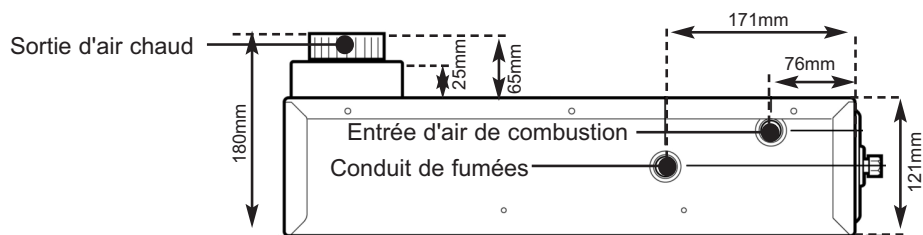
Installation sous plancher - Vue latérale - SH2211 ou SC2211
